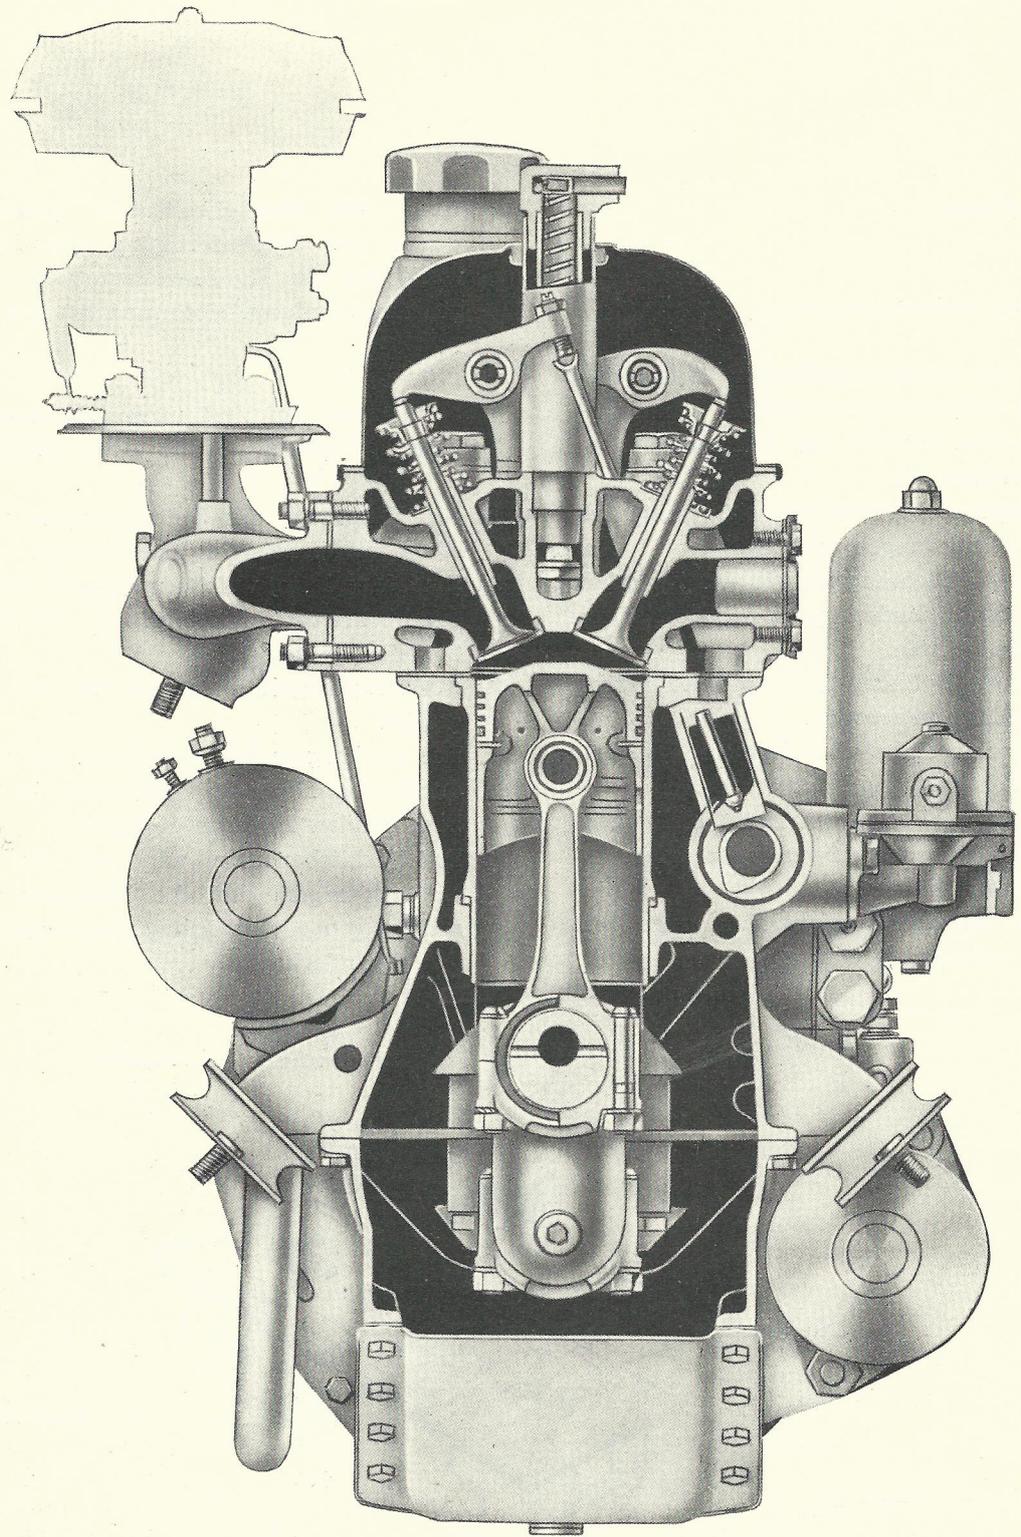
Aufgeschnittener Peugeot-Motor, Typ 203
